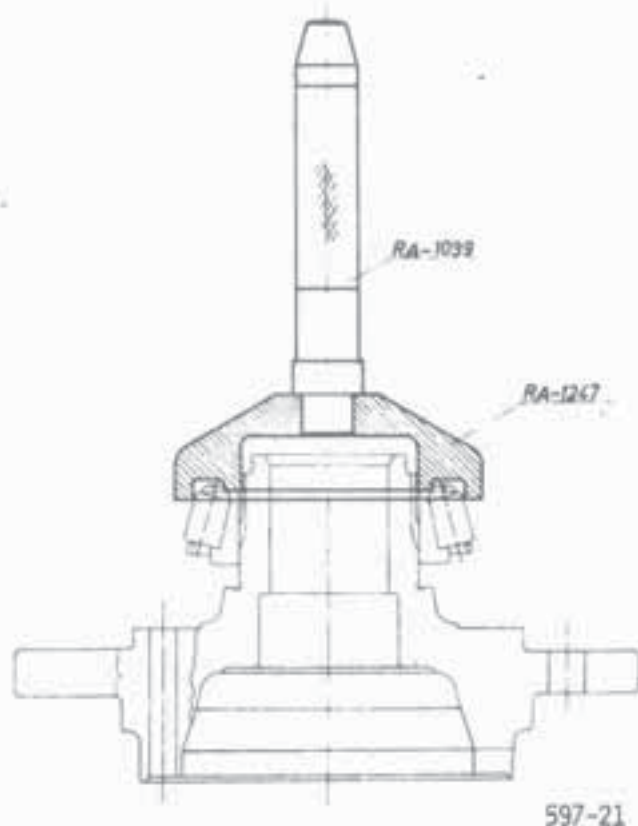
Напрессовка внутреннего кольца конического роликоподшипника
